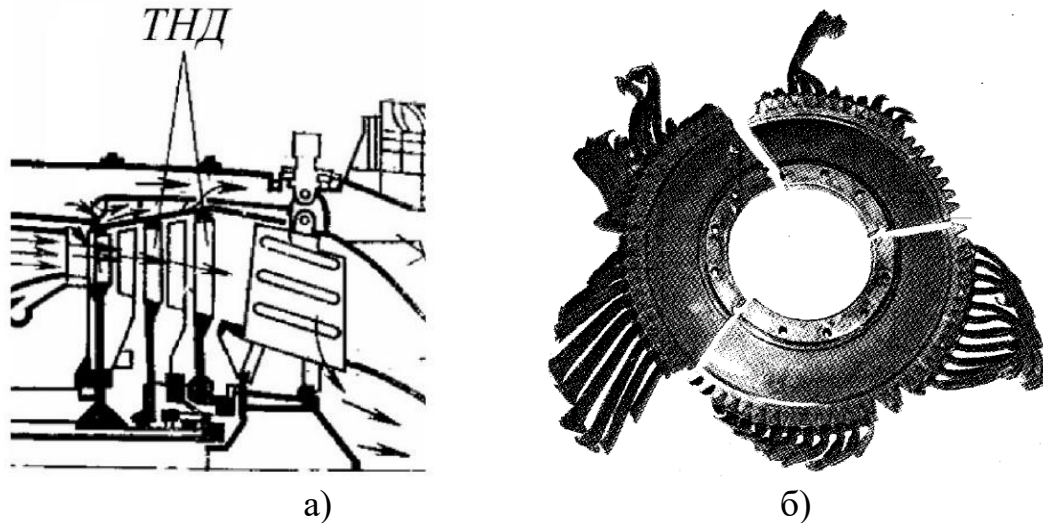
(а) Схема турбины двигателя НК-8-2У и (б) разрушенный в эксплуатации диск 2-й ступени ТНД
